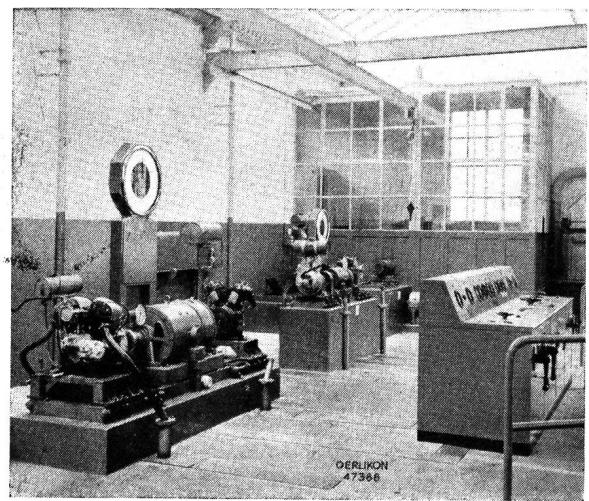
Leistungswaage in einer schweizerischen Fabrik für Explosionsmotoren.
